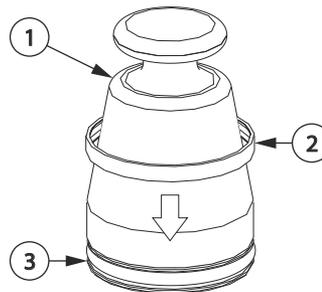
Einsetzen der äußeren O-Ring-Dichtung
